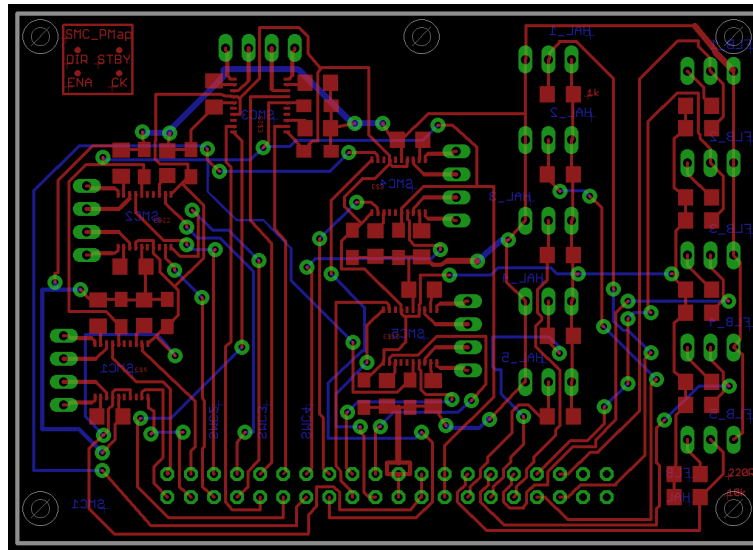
Layout der Schrittmotor-Treiber-Platine. Rot: Top-Layer; Blau: Bottom-Layer.
